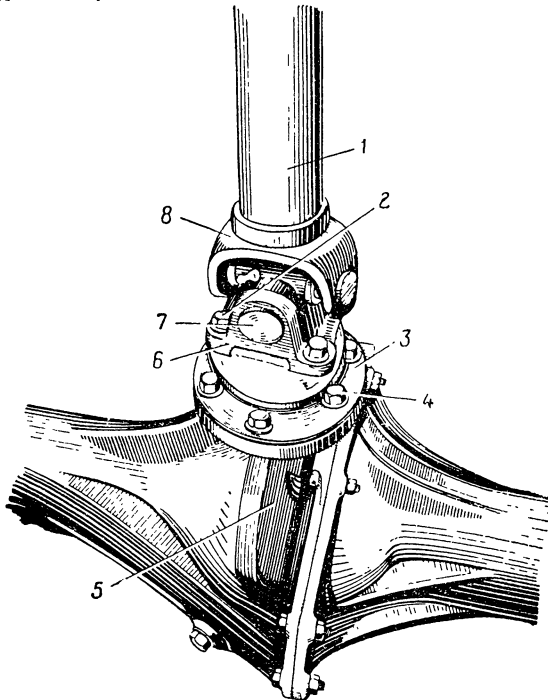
Крепление крестовины кардана к фланцу ведущей шестерни главной передачи:
